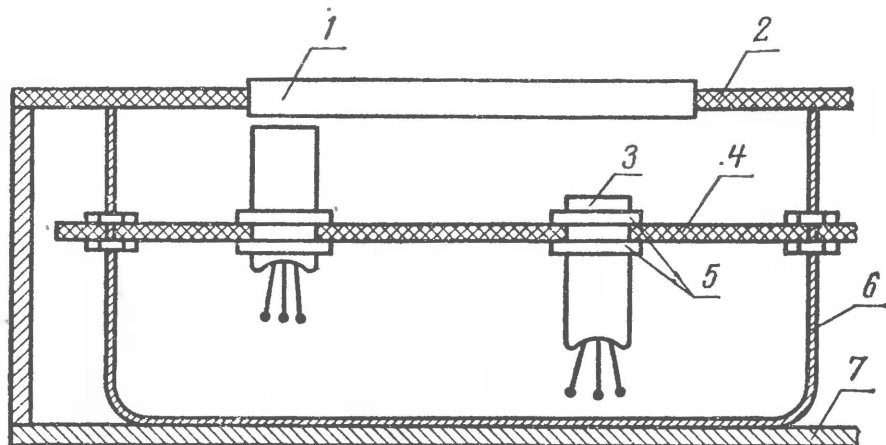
Монтаж МТХ-90 в корпусе макета: 1 — «соединительные проводники» из оргстекла; 2 — панель из винипласта; 3 — МТХ-90; 4 — панель крепления ламп; 5 — резиновые кольца; 6 — скобы из металлического прутка; 7 — корпус прибора
